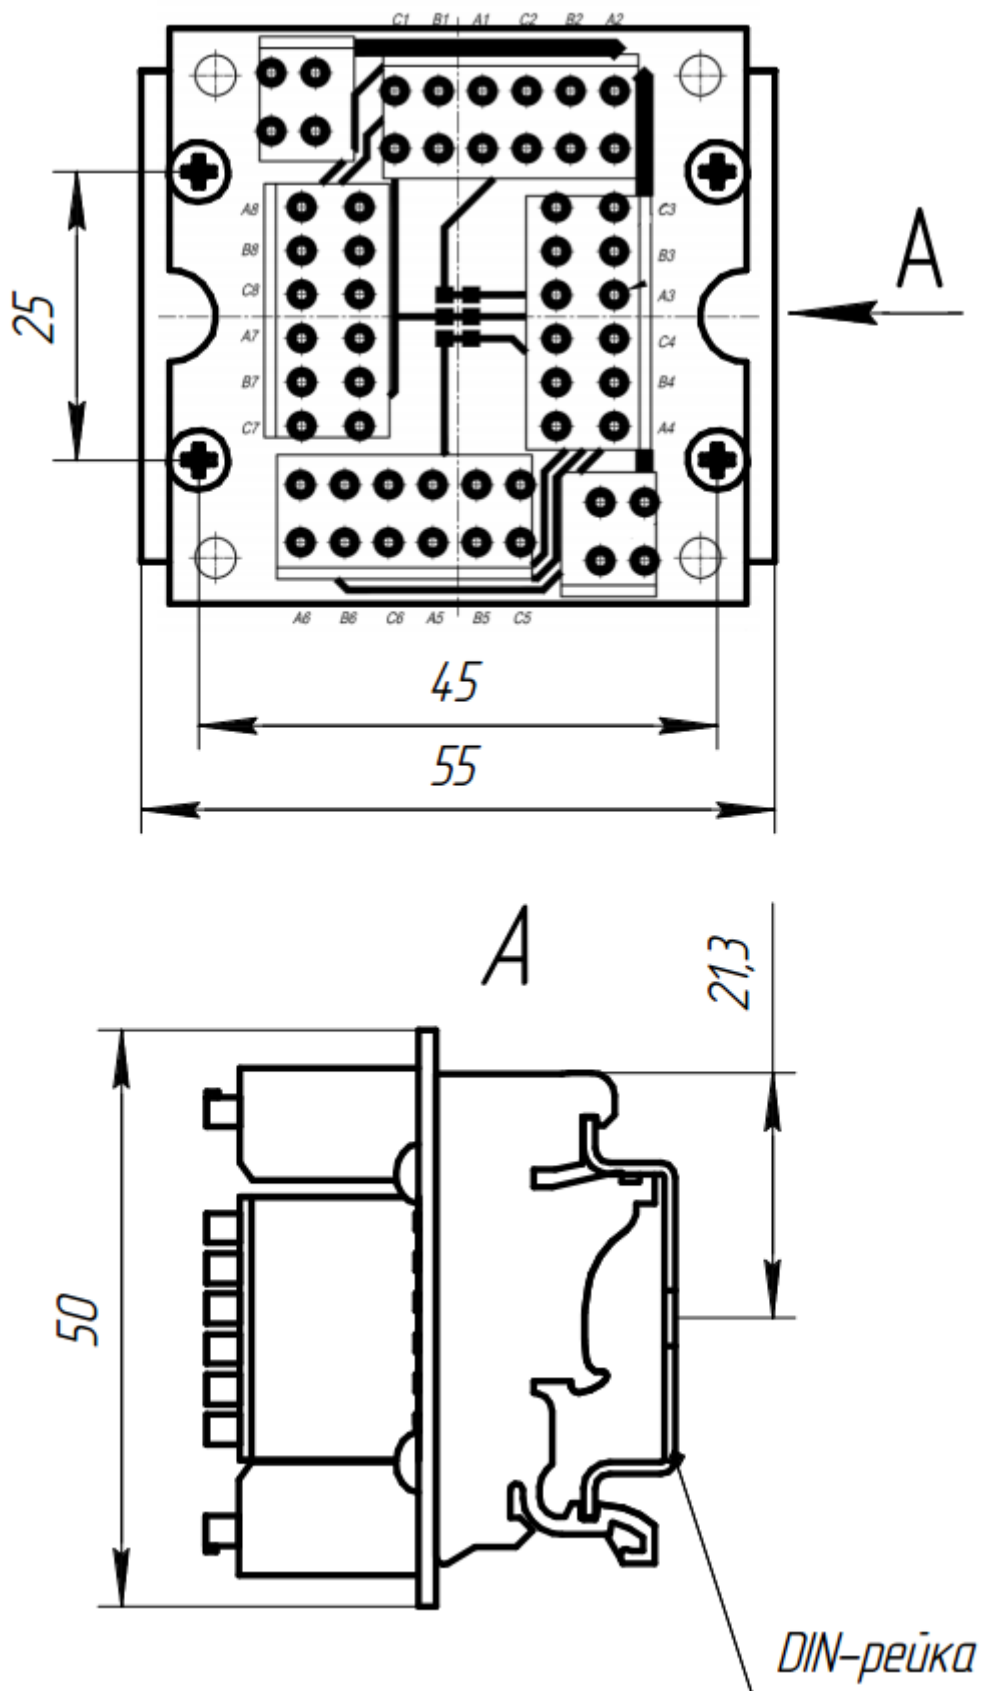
Внешний вид, габаритные и присоединительные размеры разветвительной коробки
